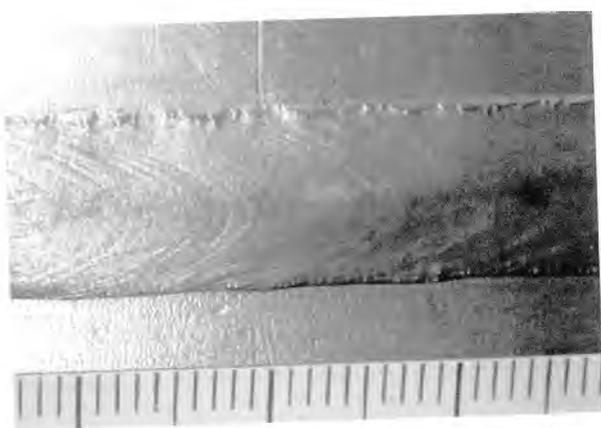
Стыковое сварное соединение обечайки сосуда. Автоматическая сварка в среде защитных газов.
